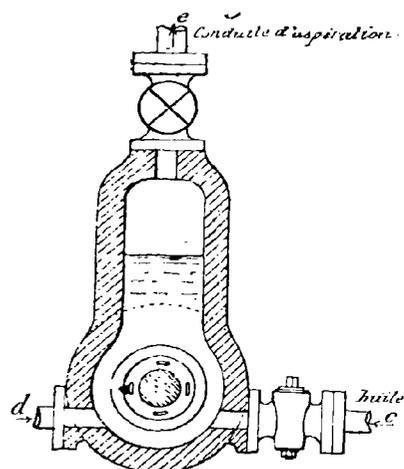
Circulation d'huile dans la lanterne du presse-étoupes Fixary.
